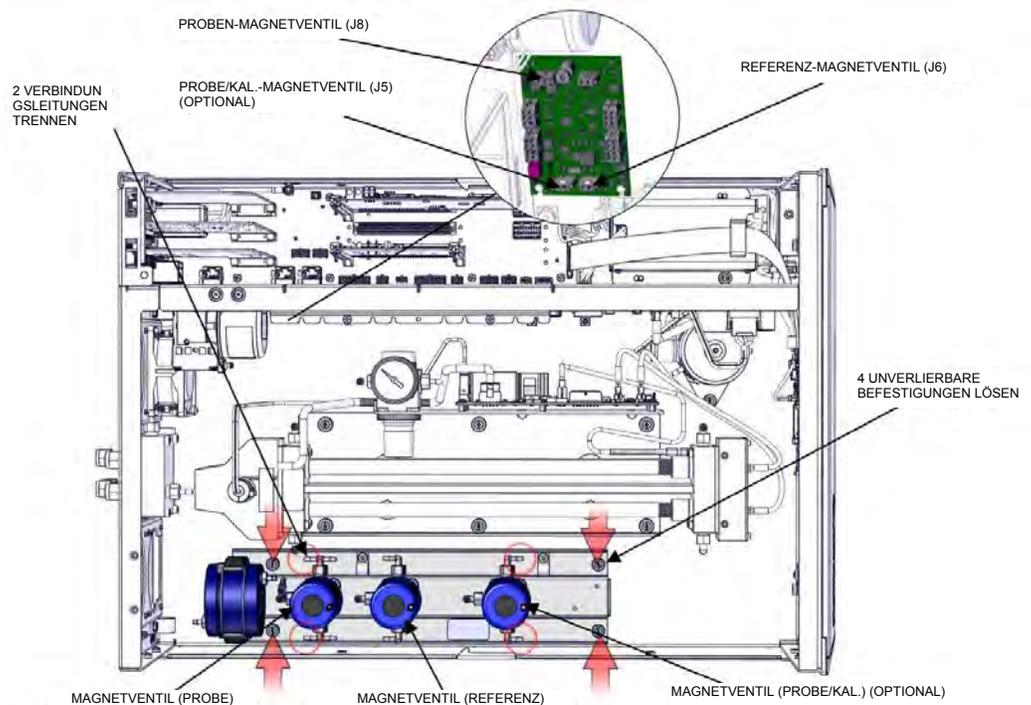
Ausbau der Magnetventilplatte, Teil 1
